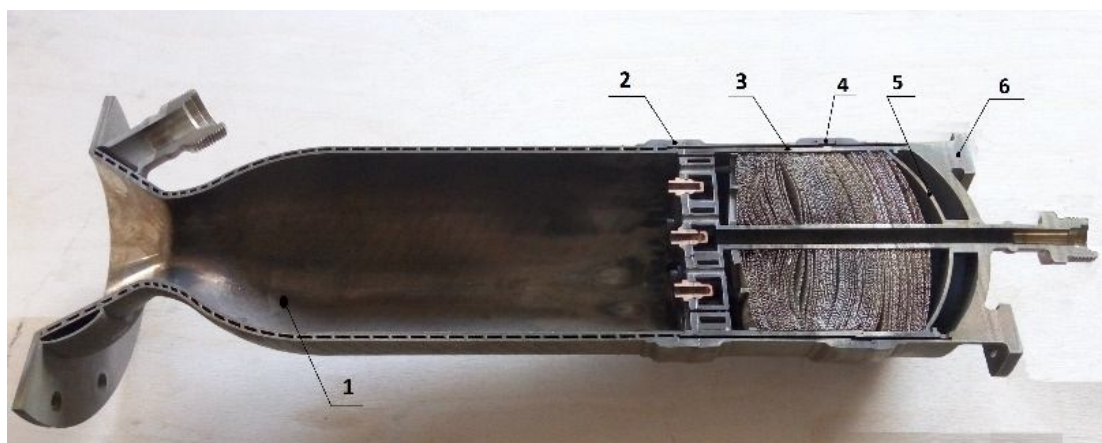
Разрез камеры двигателя после прохождения огневых испытаний
